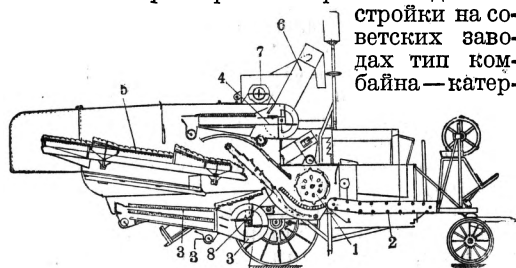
Комбайн Клейтона (разрез): 1—барабан, 2—питатель, 3—нижняя веялка, 4—верхняя веялка, 5—конвейерный соломотряс, 6—зерновой элеватор, 7—шесталка или шерстовака, 8—элеватор.
